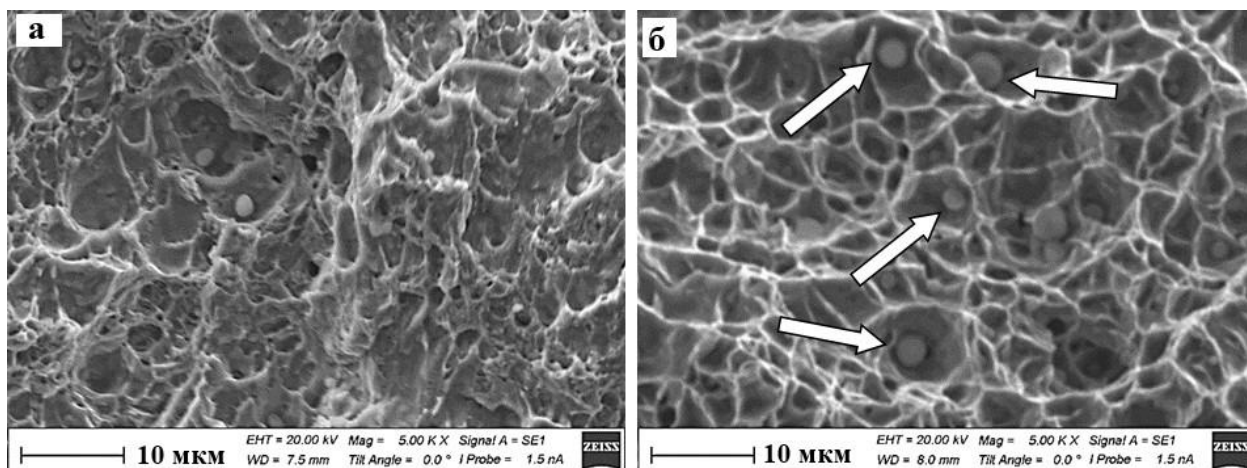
Фасетки вязкого излома металла сварного шва №1 (а) и №2 (б) (стрелками на (б) указаны частицы второй фазы)
